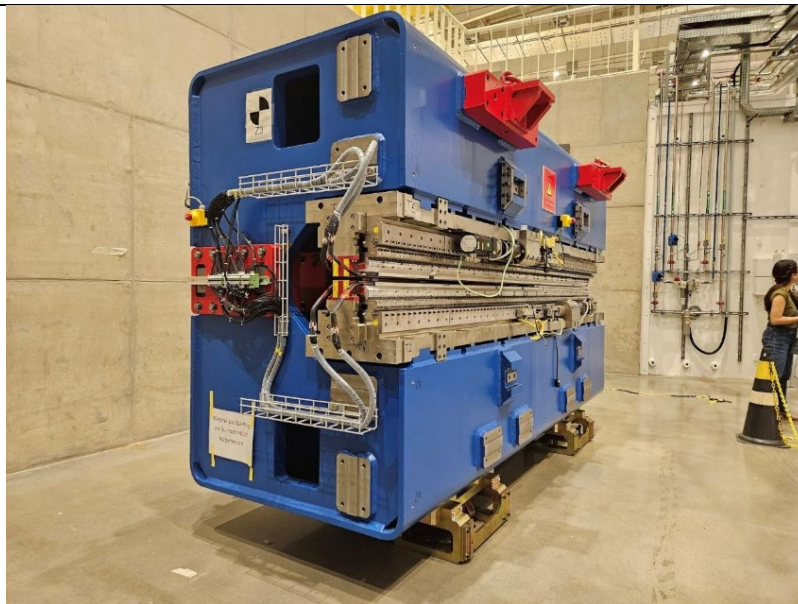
Conjunto do ondulador definitivo em área de integração/montagem, com destaque para a estrutura mecânica e interfaces laterais, em preparação para instalação e testes.
